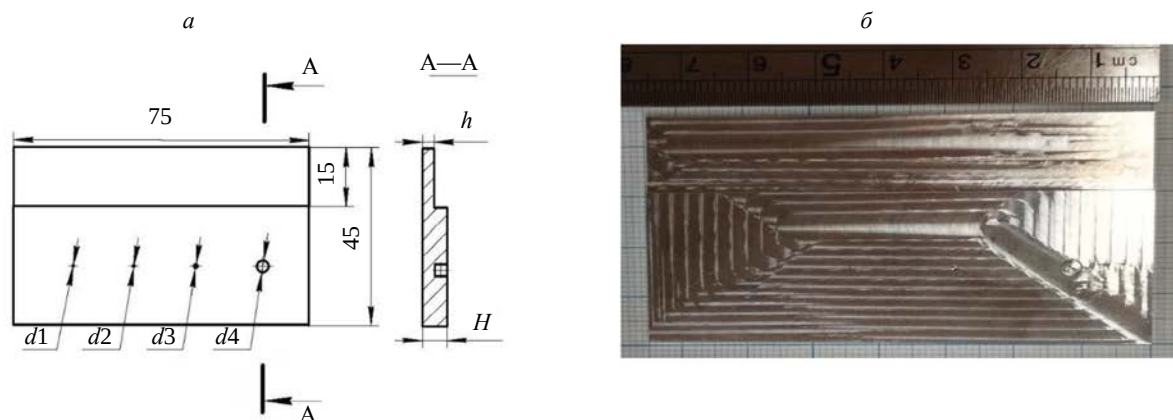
Образец настроечный с имитаторами дефектов типа непровар: эскиз (а); общий вид (б).
